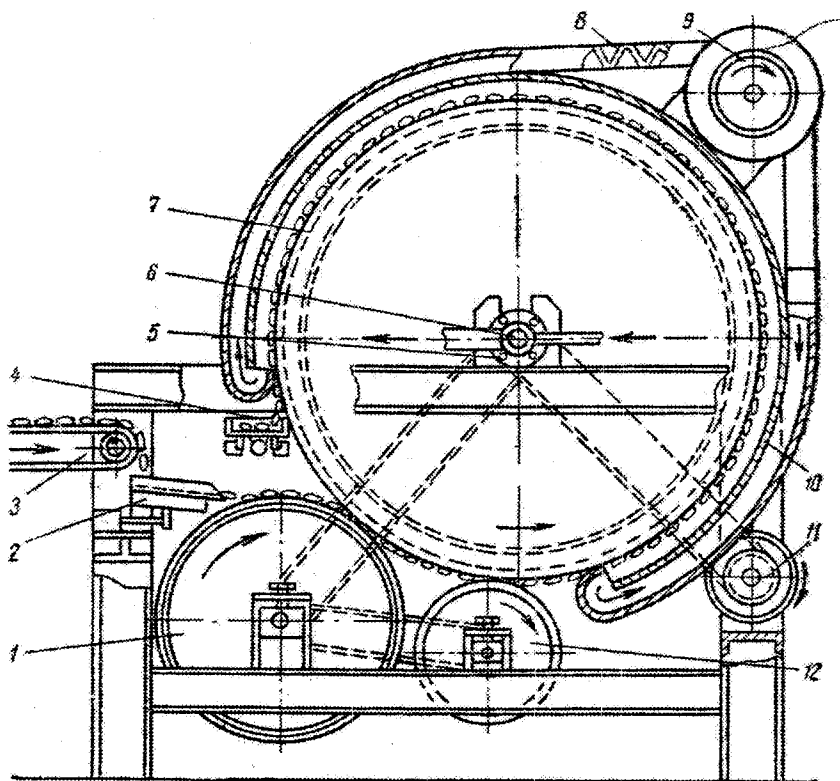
Морозильний апарат барабанного типу для заморожування вологих продуктів неправильної форми: 1 – живлячий барабан; 2, 4 – віброролки; 3 – вхідний конвеєр; 5 – підпипники; 6 – вал; 7 – заморожувачий барабан; 8 – повітроохолоджувач; 9 – вентилятор; 10 – кожух; 11 – електродвигун; 12 – притисний барабан.
